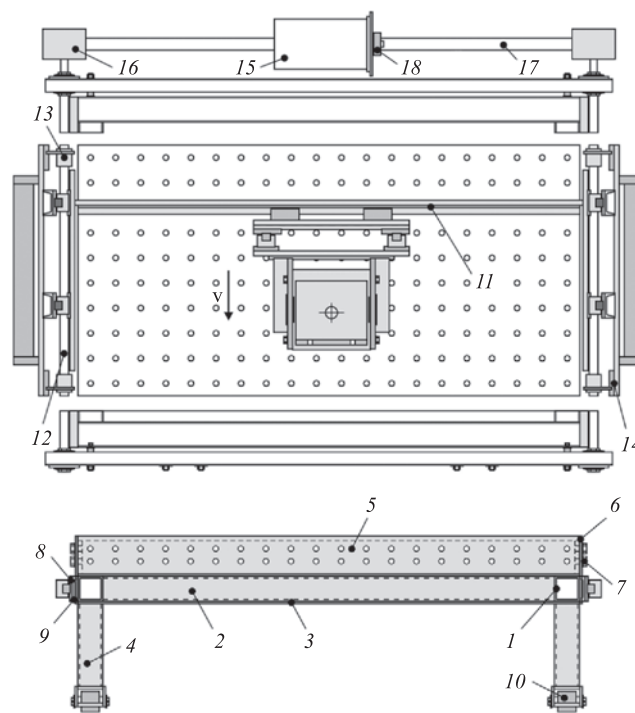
Сварочный стол и схема подачи портала по оси X
